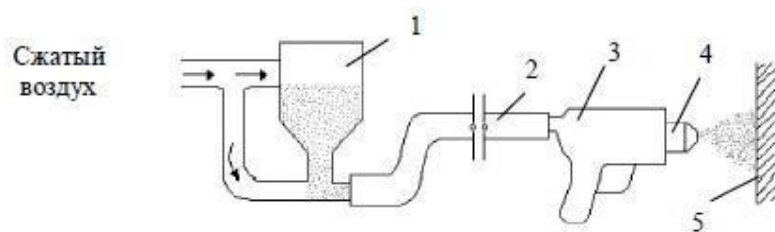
Схема пневмомеханической очистки деталей:
